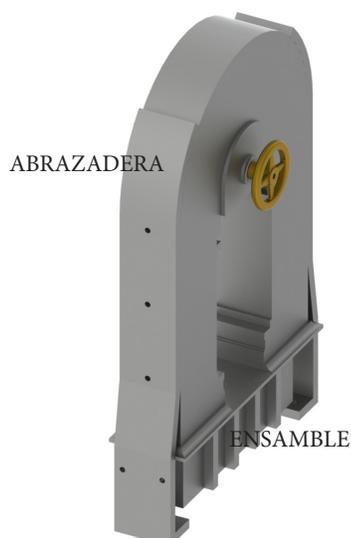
Medallón con abrazaderas y ensamble de espigas en la parte inferior
